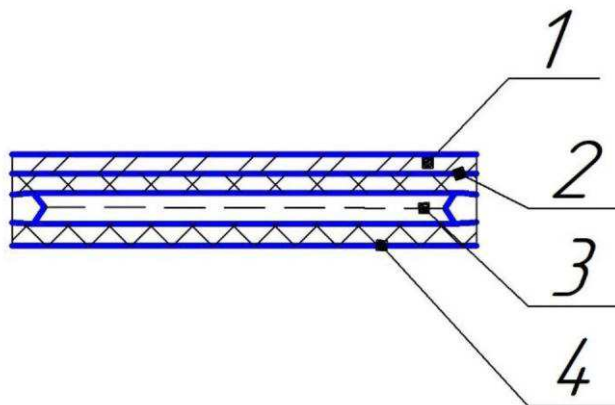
Защитный вкладыш. Вид с боковой части и в разрезе
